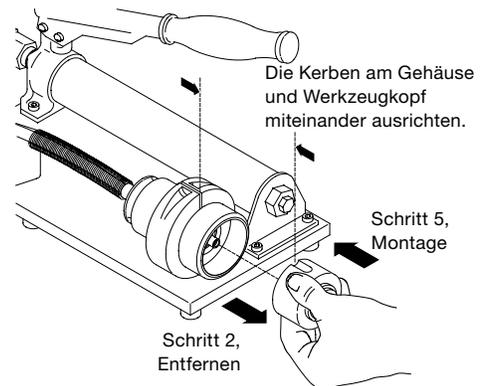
Entfernen/Einsetzen des Werkzeugkopfes
